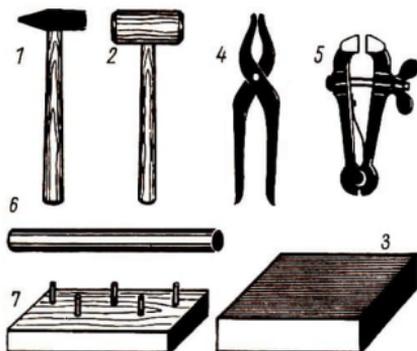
Werkzeuge und Hilfsmittel zum Richten
